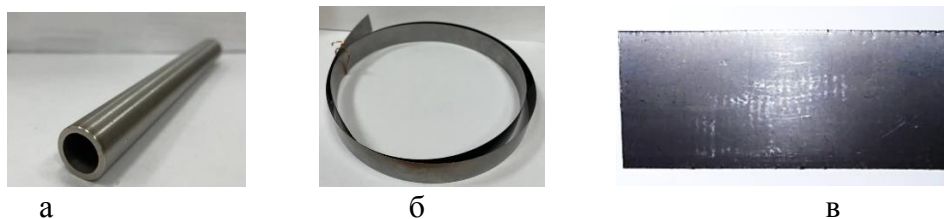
Этапы физического эксперимента: а – заготовка, б – полученная лента после прокатки, в – разрушение боковой кромки
